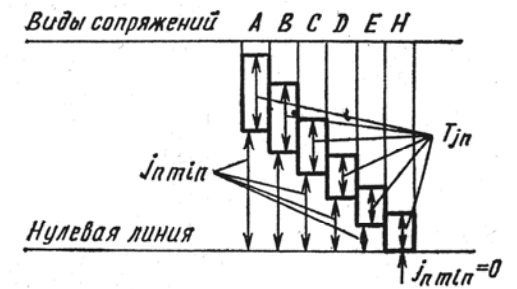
Схема расположения полей допусков T_{jn} для принятых видов сопряжений зубьев зубчатых колес
